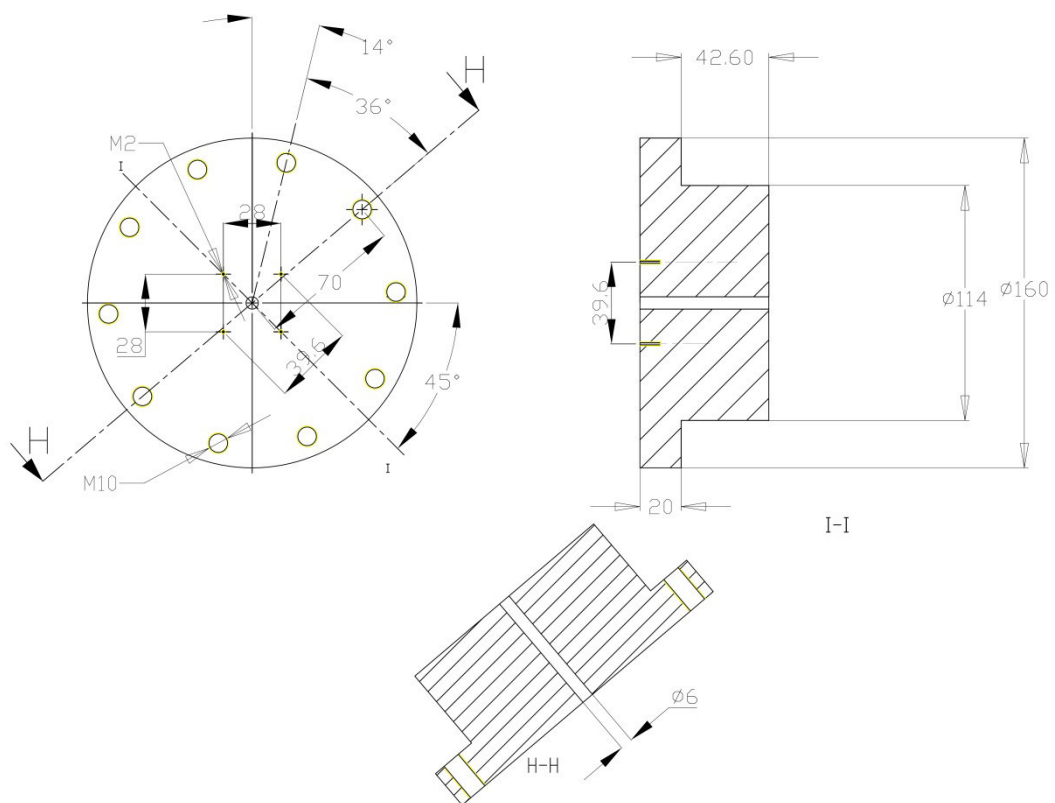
Tapa de una de las caras de la bomba de combustión cilíndrica
